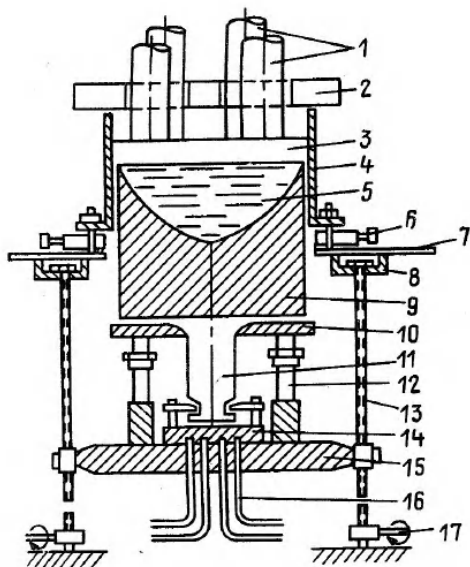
Схема печи ЭШП для получения крупного слитка: 1 - электроды, 2 - крышка; 3 - шлаковая ванна; 4 - кристаллизатор; 5 - металлическая ванна; 6 - уплотнение; 7 - рабочая площадка; 8 - опора винта; 9 - слиток; 10 - стол; 11 - заправка-стержень; 12 - плунжер гидросистемы; 13 - винт; 14 - контактная плита; 15 - стол; 16 - токоподвод; 17 - привод винта
